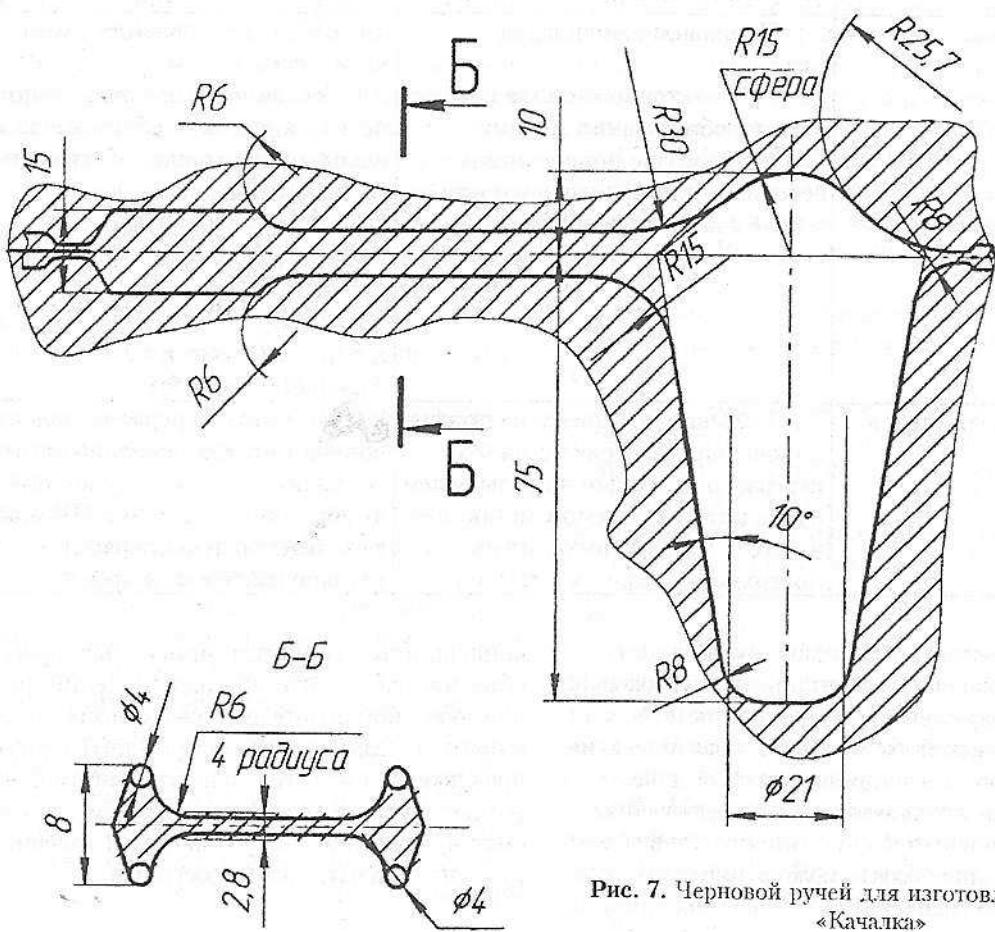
Черновой ручей для изготовления поковки «Качалка»
